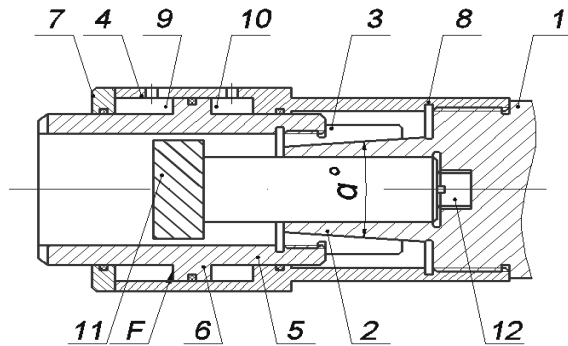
Безкамерний гідромеханічний затискний патрон
